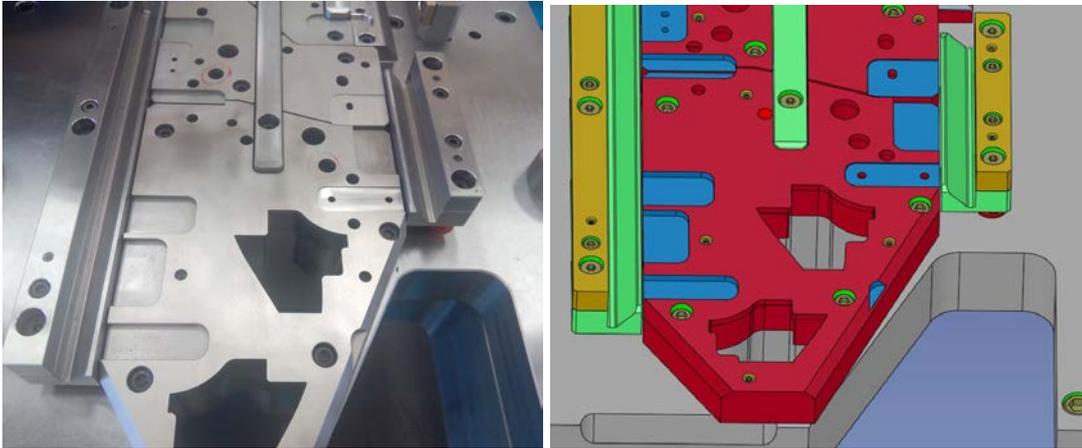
Detalle del montaje de la matriz de punzonado y separación de pieza
